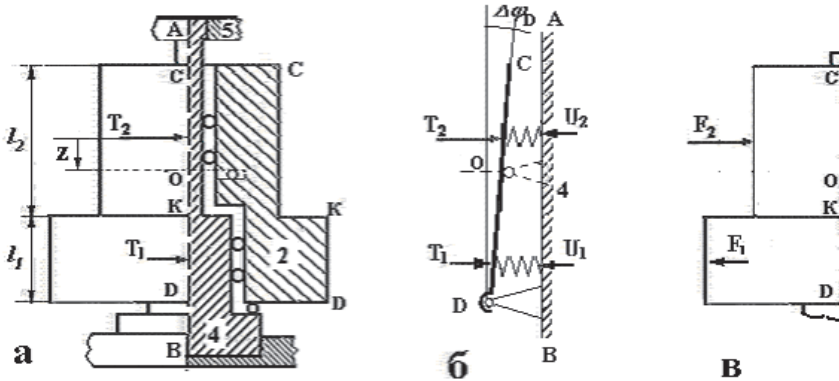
Силы, действующие на корпус промежуточной шестерни.
